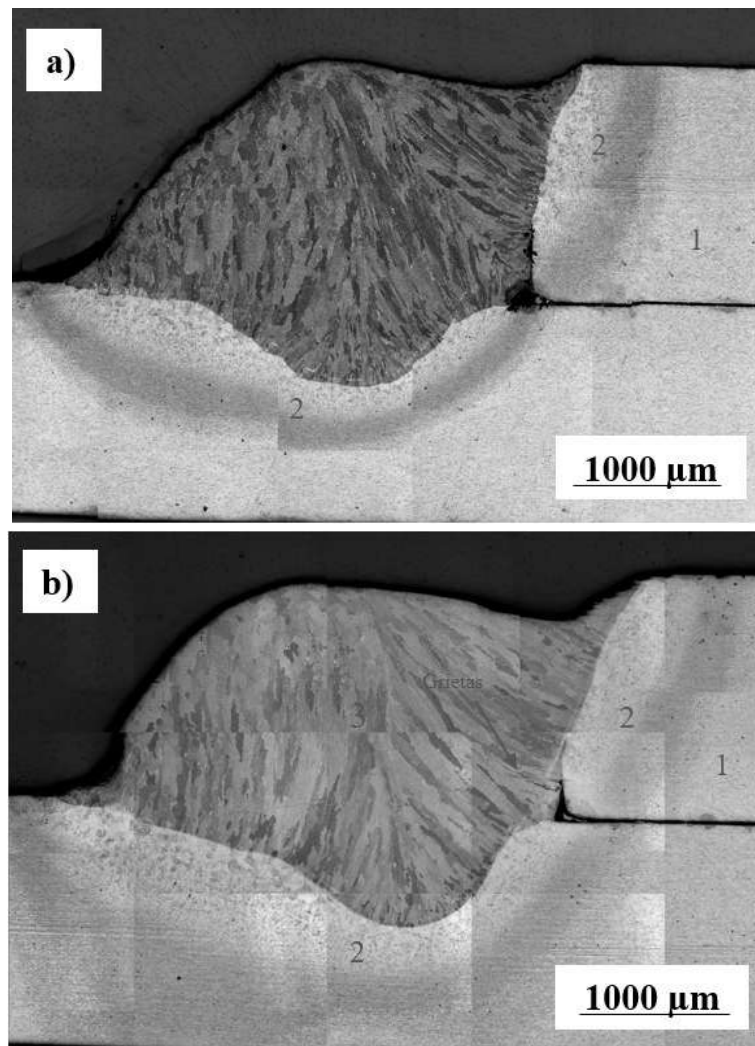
Macrografías de las uniones soldada con el electrodo ER80S-D2 mediante el proceso de soldadura GMAW-P, tomadas con MO a 5x, a) C1 b) C2.
